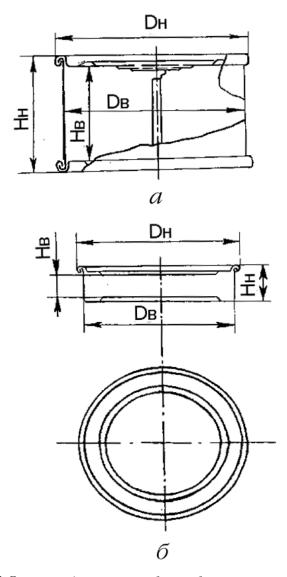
Банка цилиндрическая: а – сборная; б – цельноштампованная
